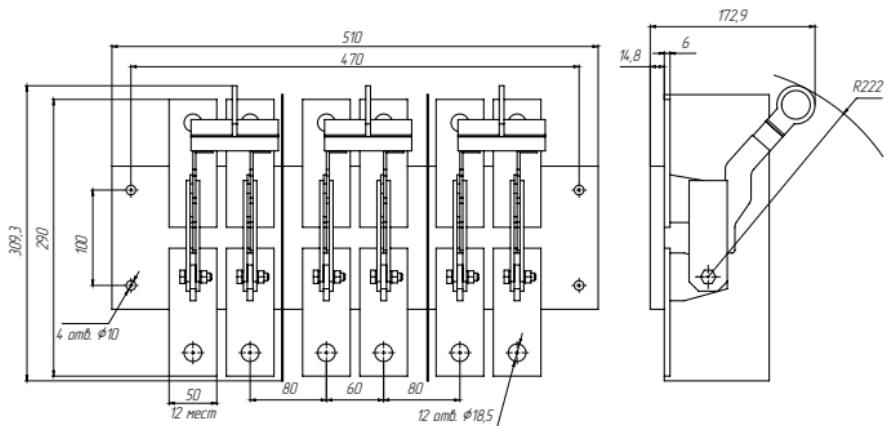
Габаритные и установочные размеры разъединителя типа РЕ19-44/45/46-31160 с рычагом для пополюсного оперирования штангой
